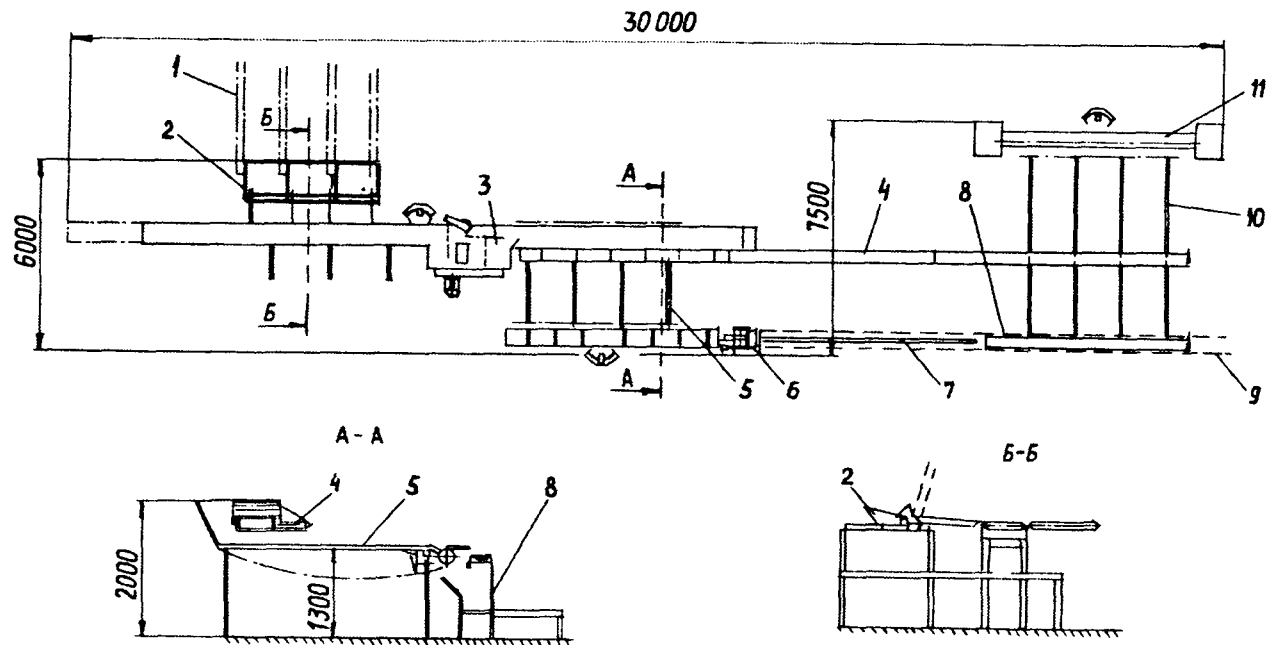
Схема участка лесопильного цеха с круглопильным станком Kara-Master:
